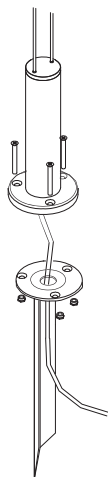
СХЕМА МОНТАЖА СВЕТИЛЬНИКА К КОЛЫШКУ LUCYLLE
